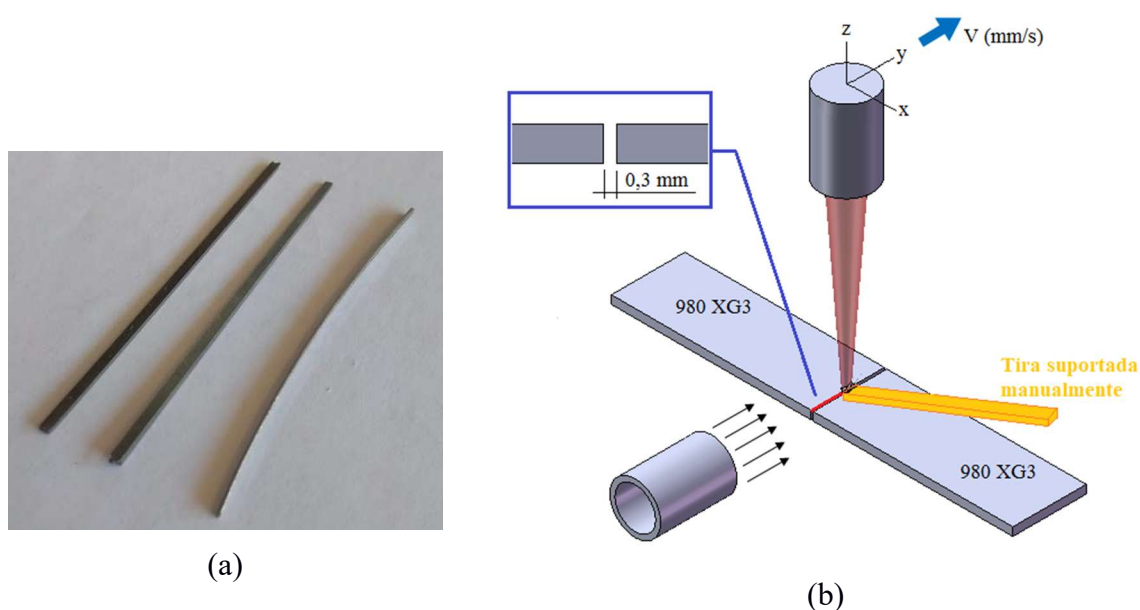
(a) Tiras utilizadas para a soldadura MA10. (b) Procedimento seguido para a soldadura MA10
